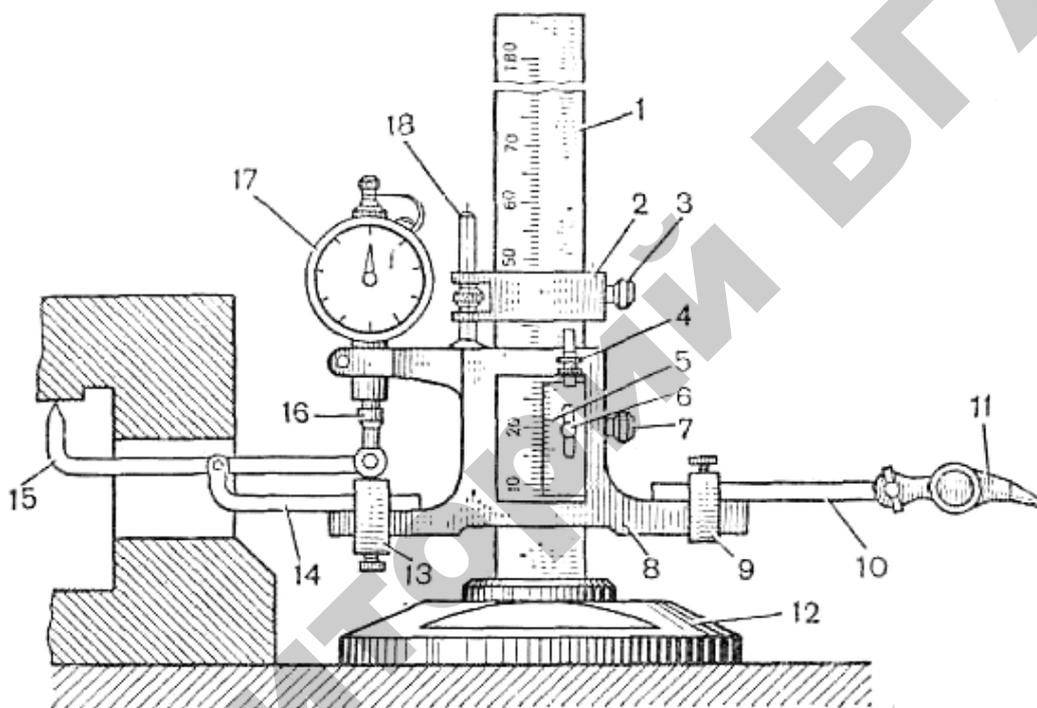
Штангенрейсмус с индикаторным устройством
